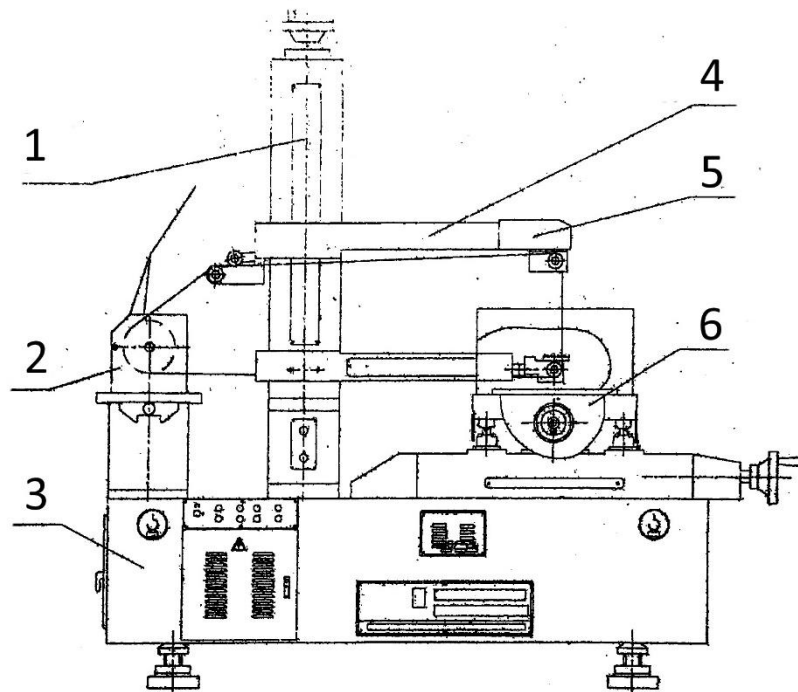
Проволочно-вырезной станок с ЧПУ типа DK77 с малым углом конусности: 1 – вертикальная опора проволоки (колонна); 2 – система протяжки проволоки; 3 – основание(станина); 4 – верхняя опора проволоки (верхний рукав); 5 – конусное устройство (система угла наклона проволоки); 6 – рабочий стол.
